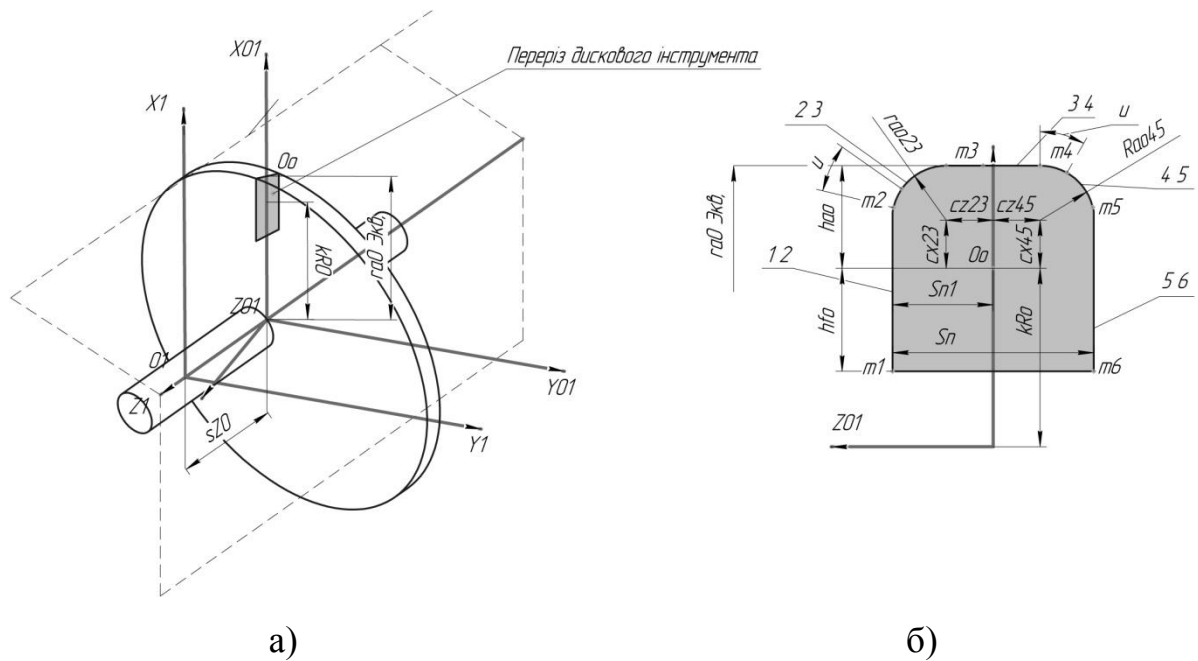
Схема утворення вихідної інструментальної поверхні загального випадку – дискового інструмента
